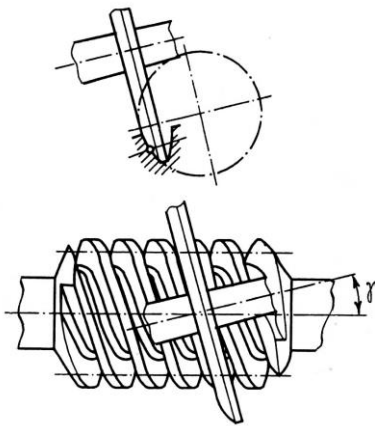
Схема обработки нелинейчатого червяка ZT с вогнутым профилем витка
